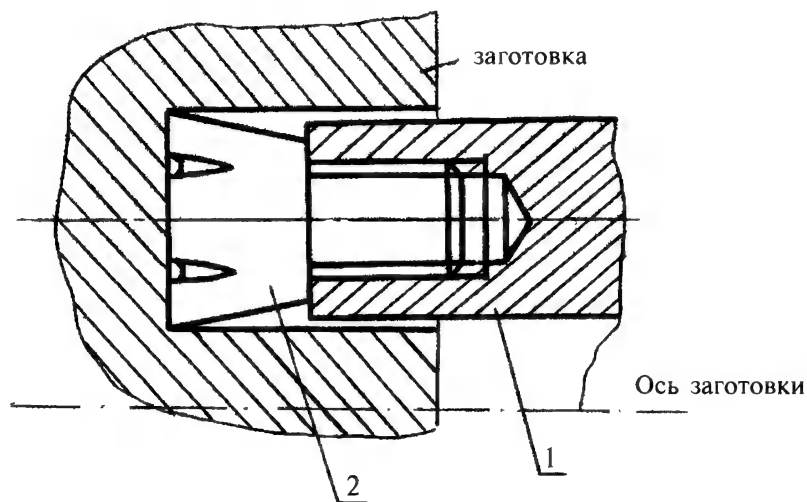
Корончатая сверлильная головка для кольцевого сверления:
